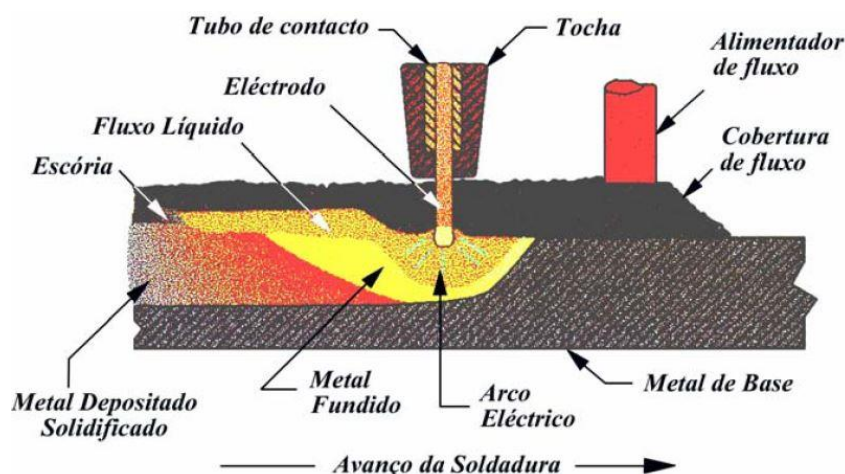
Representação esquemática da soldadura por arco submerso
